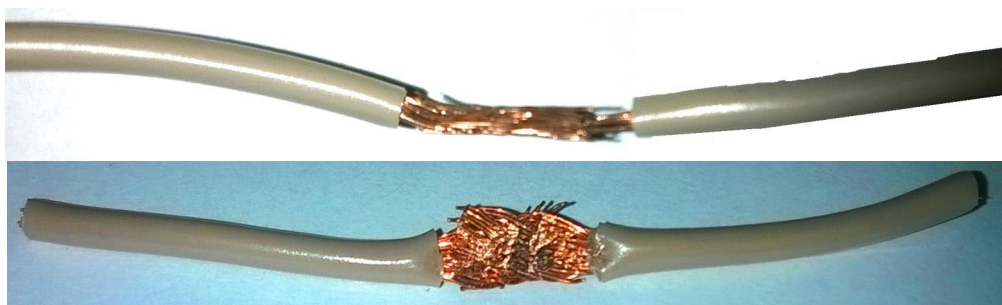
Многожильный медный провод сваренный ультразвуковой сваркой
